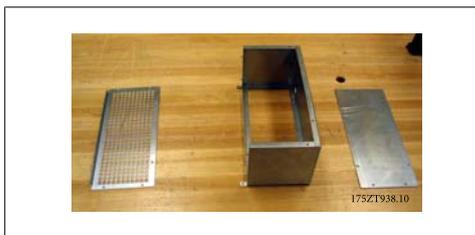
Tubulação superior parcialmente montada com suporte do conversor de frequência
